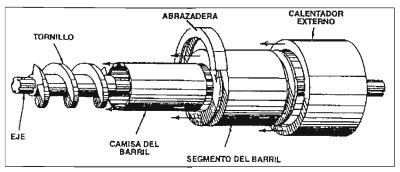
Eje de soporte del extrusor de un tornillo (http://www.aces.uiuc.edu/asamex/extrusion)
